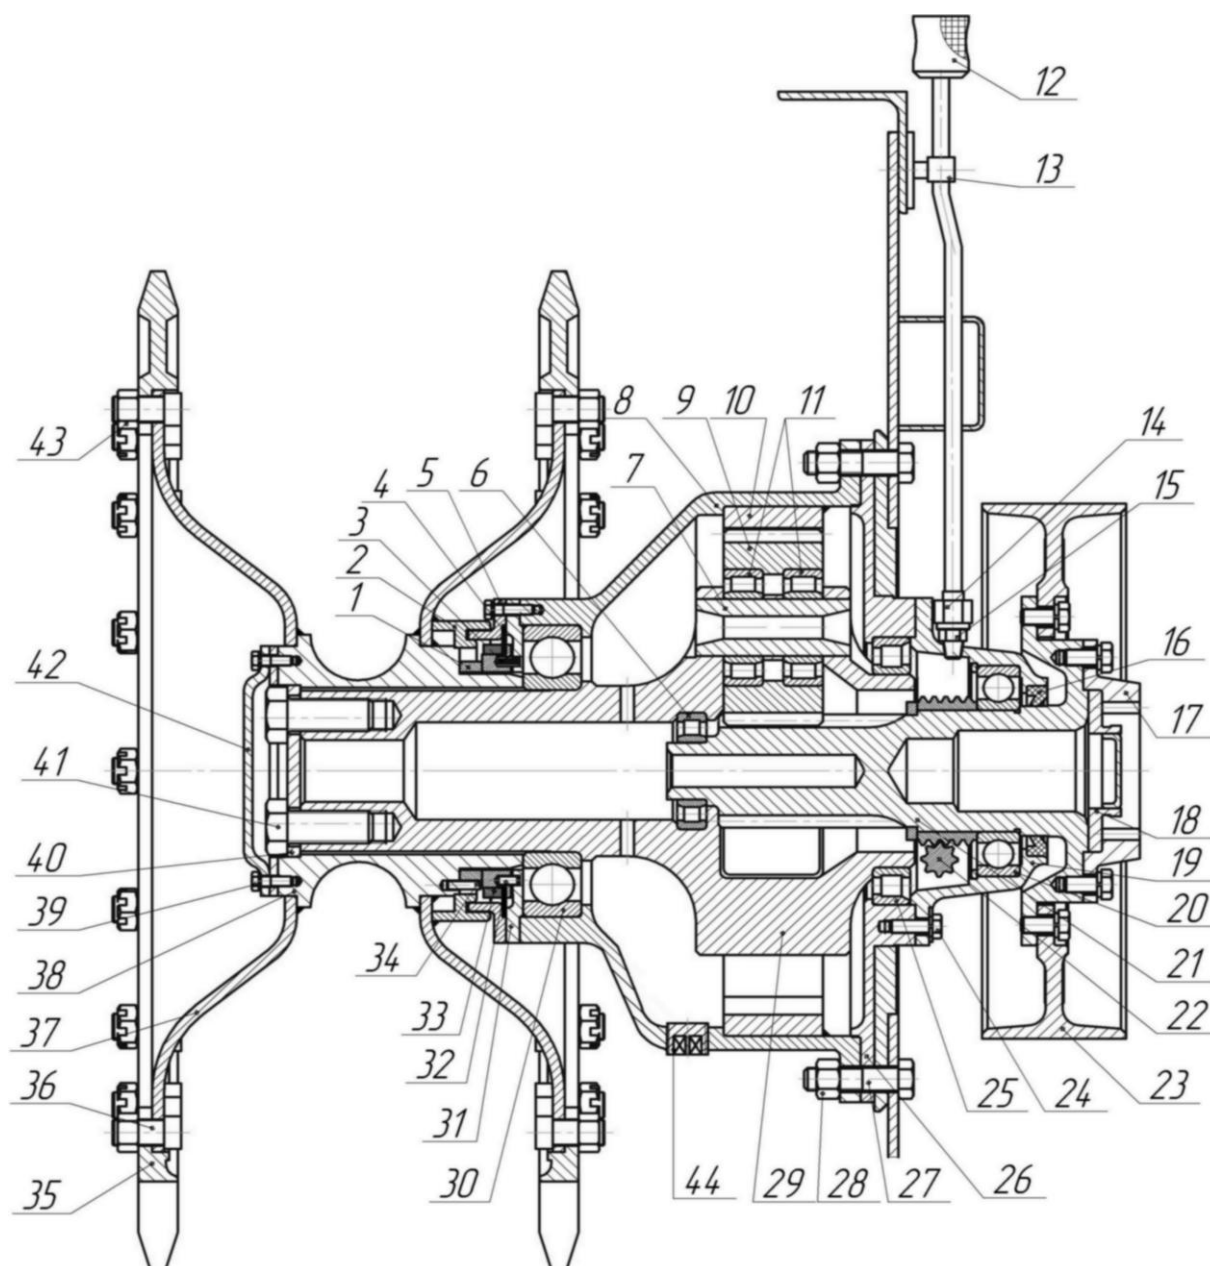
Бортовая передача (левая) с ведущим колесом:
